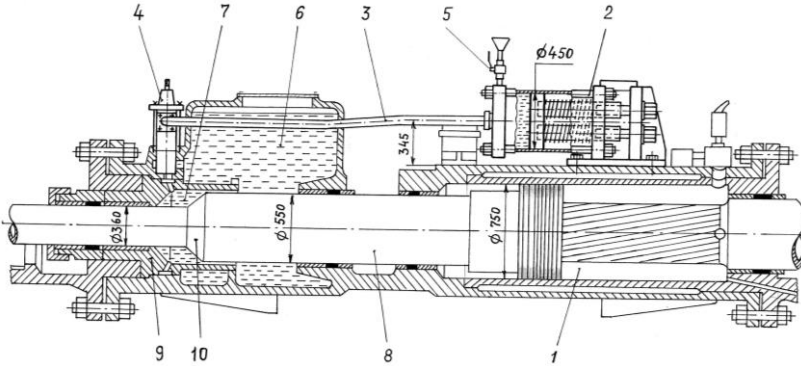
Повітряний робочий циліндр подавального апарата з пружино-гідравлічним буфером: 1 – камера повітряного циліндра (поршнева порожнина); 2 – буфер; 3 – трубопровід; 4 – запірний вентиль; 5 – шаровий кран; 6 – водяна камера; 7 – камера гальмування; 8 – шпиндель (плунжер); 9 – гальмівна втулка; 10 – уступ шпинделя.
